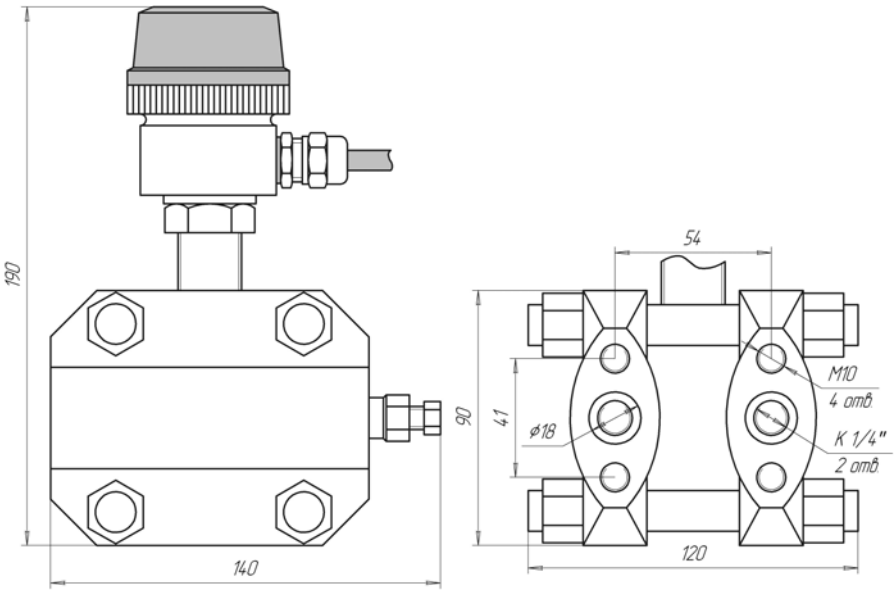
Модель 1163. Нержавеющий корпус, герметичный встроенный кабель.
